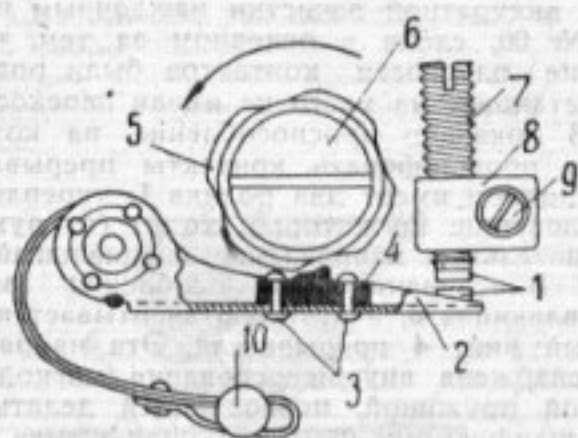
Сработавшаяся фибра на рычажке прерывателя (типа ИГФ-4003). Одна из заклепок, крепящих фибру на рычажке прерывателя, касается граней кулачка. 1—контакты прерывателя; 2—рычажок прерывателя; 3—заклепки фибры; 4—фибра (имеет сработанный выступ); 5—кулачок прерывателя; 6—винт кулачка прерывателя; 7—регулируемый контактный винт; 8—наковальня; 9—стопорный винт регулируемого контакта; 10—штифт пружины рычажка прерывателя
